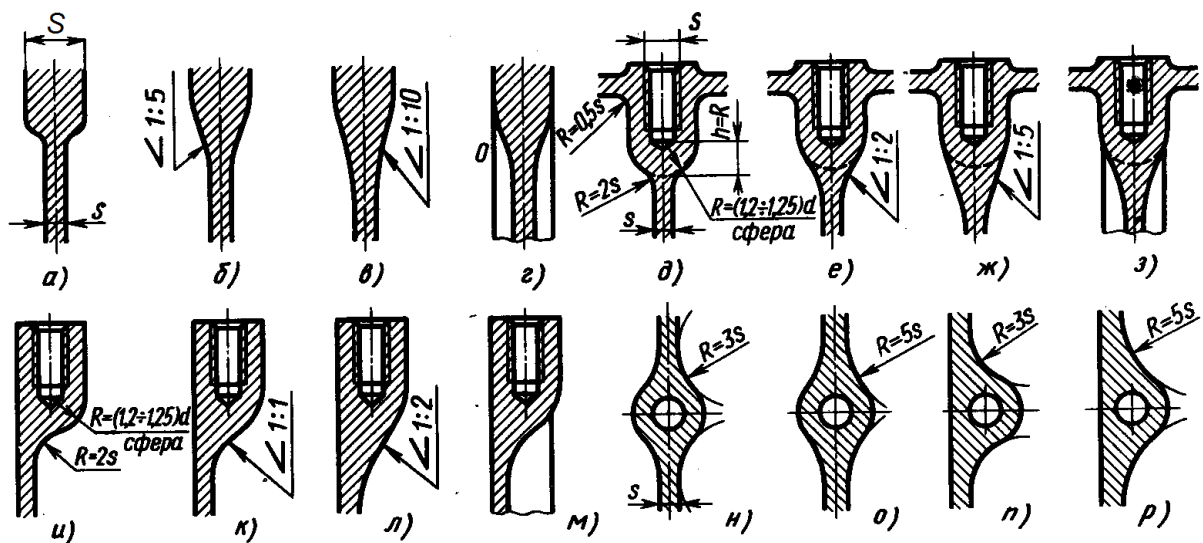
Схема сопряжения участков отливки различной толщины
